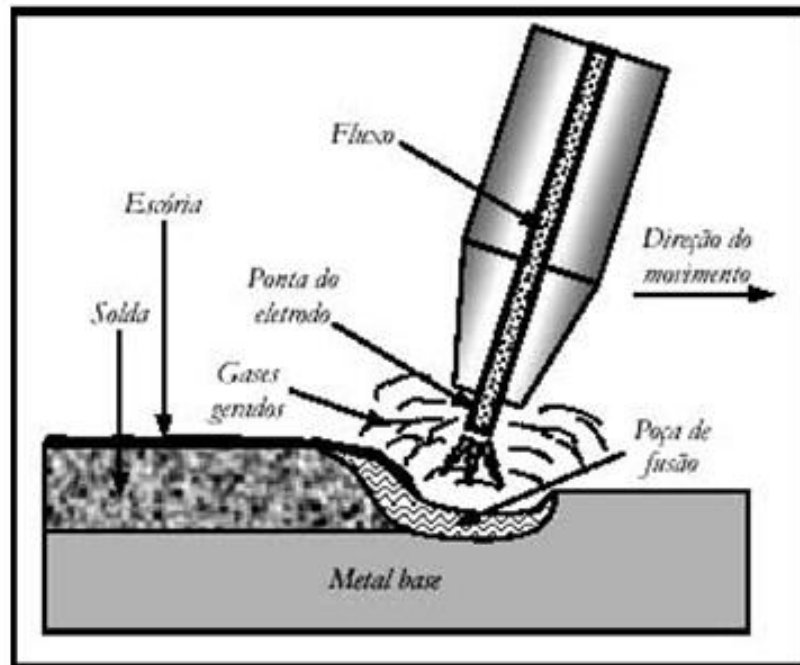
Representação esquemática do processo de soldagem a arco com eletrodo tubular
